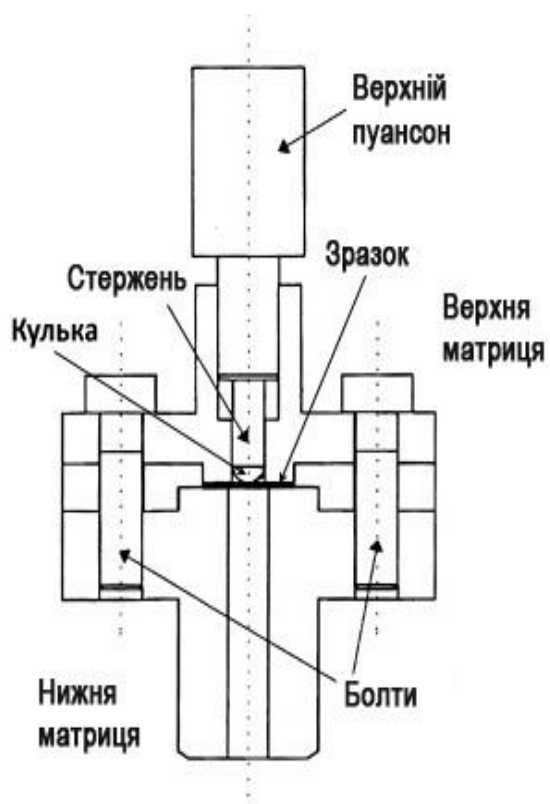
Загальна схема форми для Small Punch Test [68]–[69]
